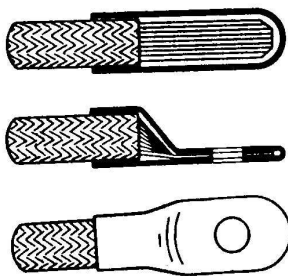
Terminal constituido por tubo aplastado con el conductor y taladrado posteriormente.
